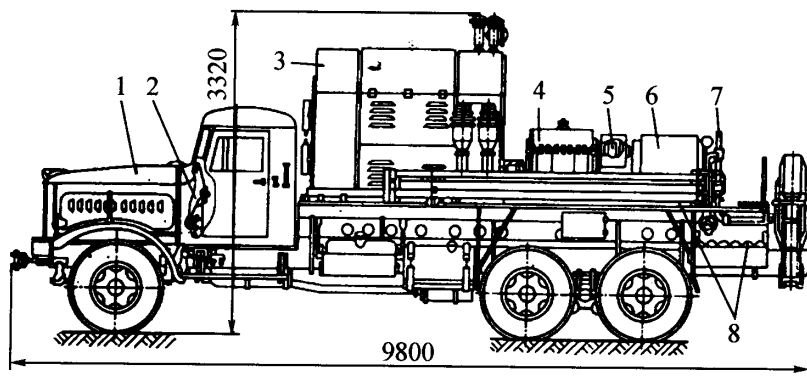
Насосная установка УН-1-630 на 700А: 1 – автошасси КрАЗ-257; 2 – пост управления; 3 – силовой агрегат; 4 – коробка передач ЗКПМ; 5 – зубчатая муфта; 6 – насос 4Р-700; 7 – напорный трубопровод; 8 – вспомогательный трубопровод
